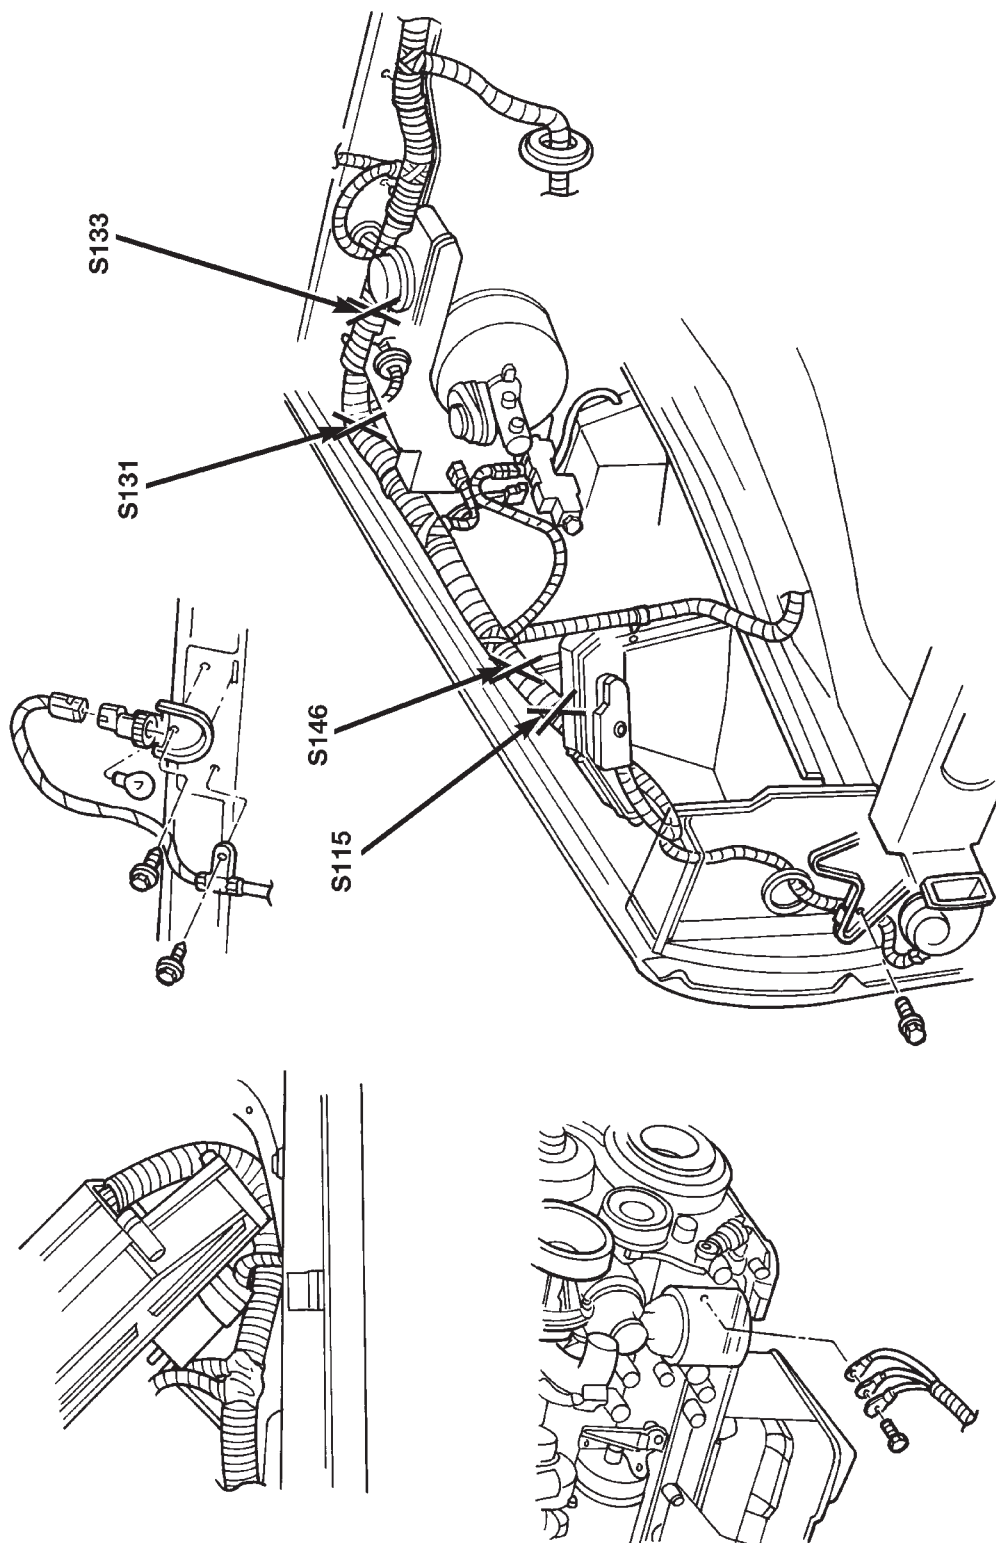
Kabelverbindungen Motorraum rechts—Dieselmotor Rechtslenker
